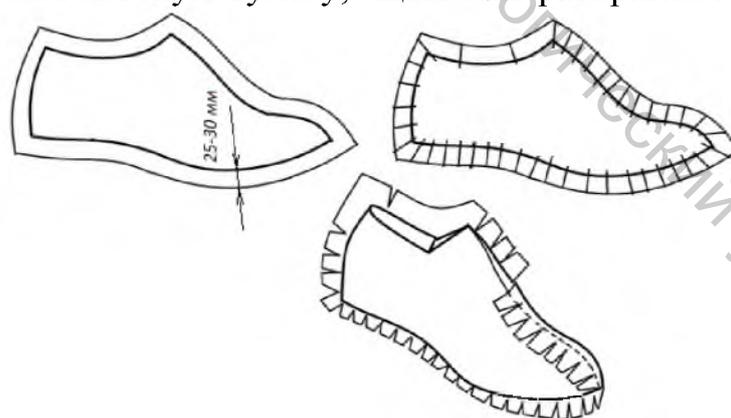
Этапы подготовки бумаги и оклеивания колодки для получения условной развертки боковой поверхности колодки
